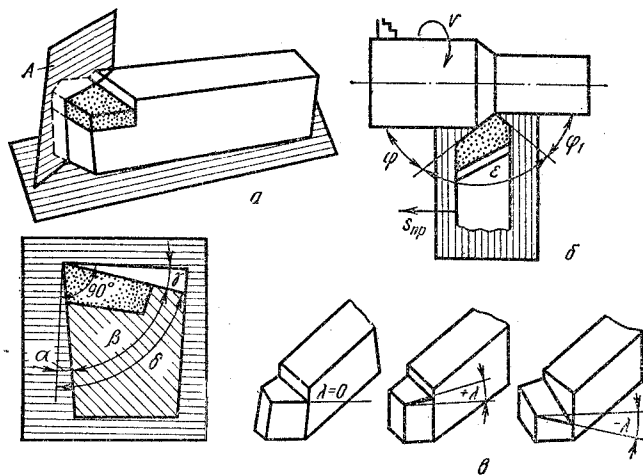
Углы заточки режущей части резца: а — главные углы; б — углы в плане; в — угол наклона главного режущего лезвия
